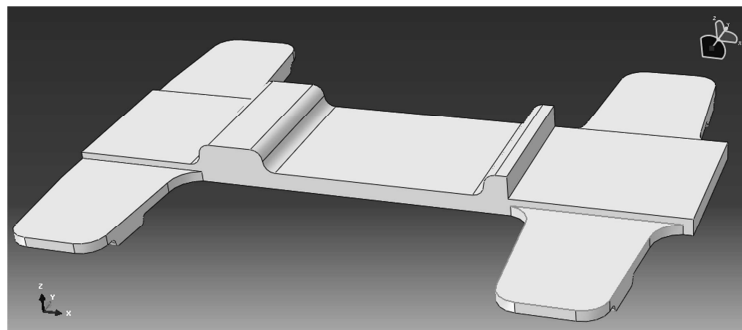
Розгортка деталі з розмірами (вигляд спереду)
